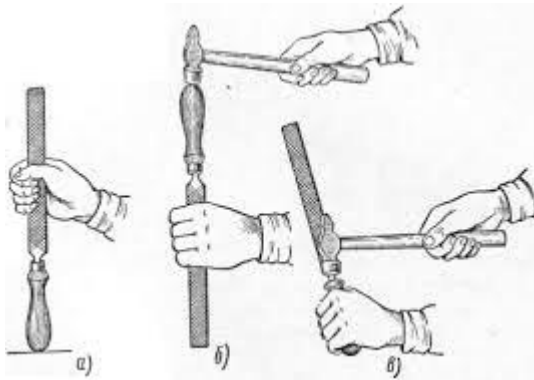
Насадка та зняття рукоятки з напилка:
